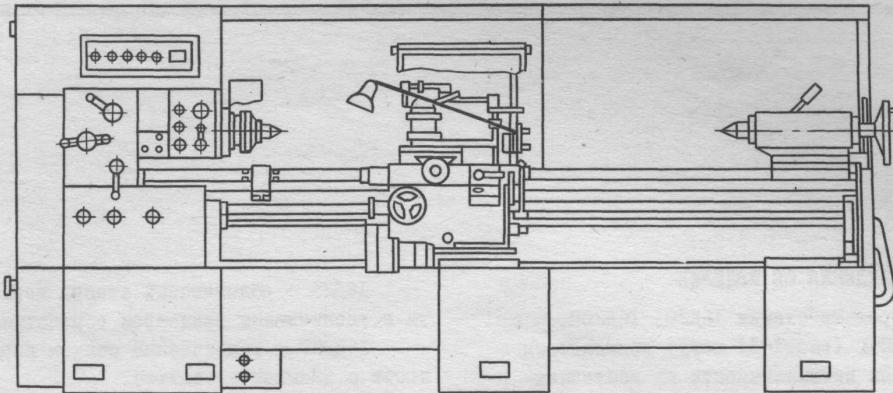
Станок токарно-винторезный I6D25 с длиной обработки L = 2000 мм
